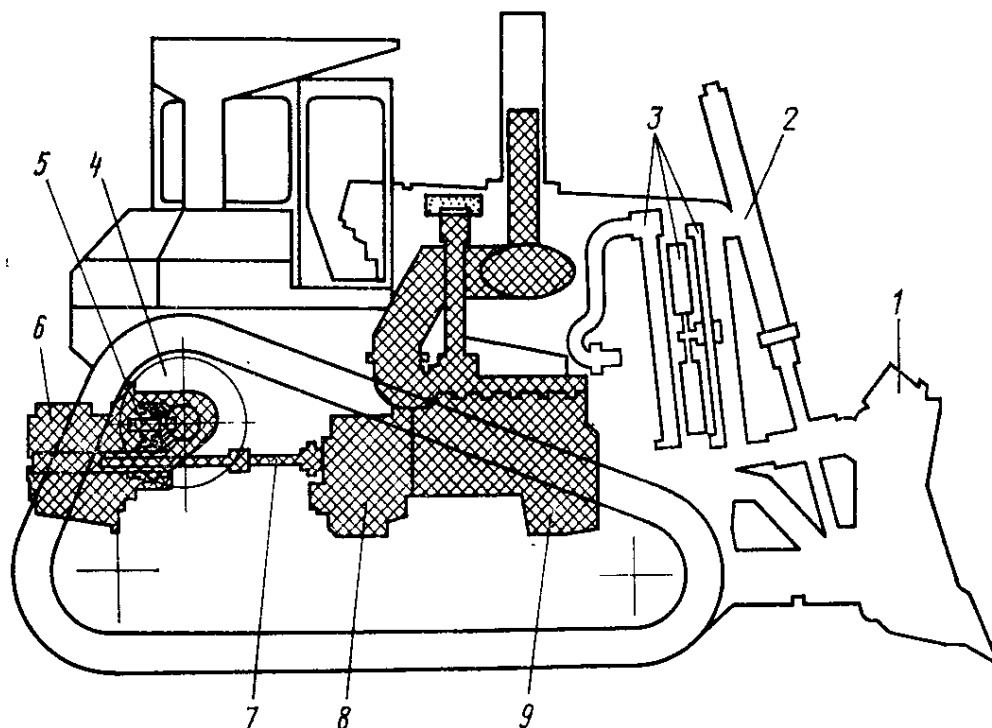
Компоновочная схема гусеничных тракторов общего назначения: 1 – отвал бульдозера; 2 – гидроцилиндры; 3 – радиаторы и вентилятор; 4 – механизмы поворота и конечные передачи; 5 – центральная передача; 6 – коробка передач; 7 – соединительный вал; 8 – гидротрансформатор; 9 – двигатель
